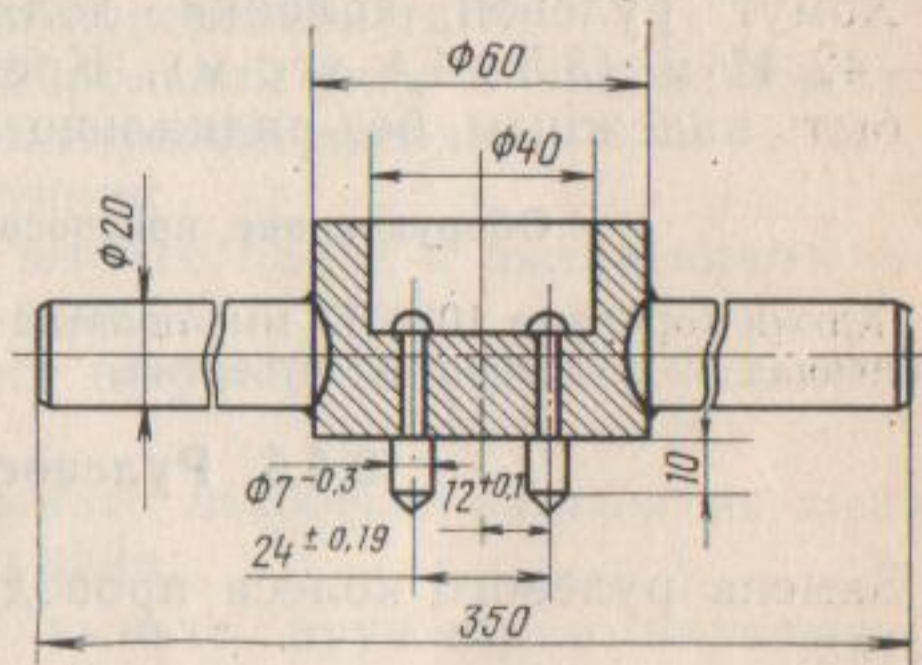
Ключ специальный для гайки шарнира гидроцилиндра рулевого управления
